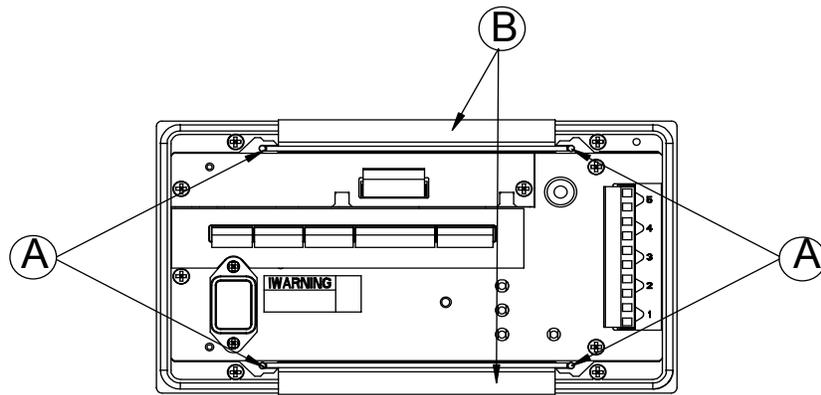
Schéma d'Installation du Montage sur Panneau
